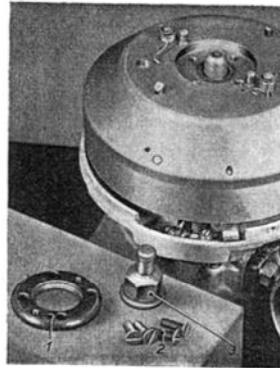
Anker Mutter (3) u. Abzugplatte (1), welche durch 4 Schrauben (2) am Glockenanker gehalten ist; wird nach Abnehmen des Unterbrecherradnocks und der Fliehkraftgewichte die Anker Mutter nach links gedreht, so kommt sie zur Anlage an der Abzugplatte, bei weiterer Linksdrehung erfolgt das Abziehen des Ankers
